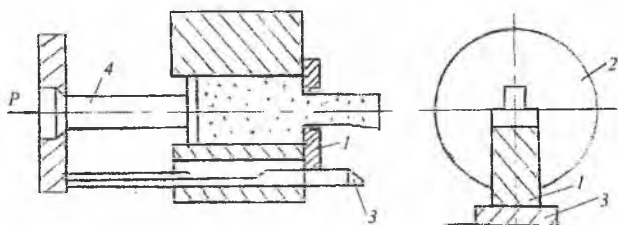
Схема прессования *T*-образного профиля с переменной толщиной полки
